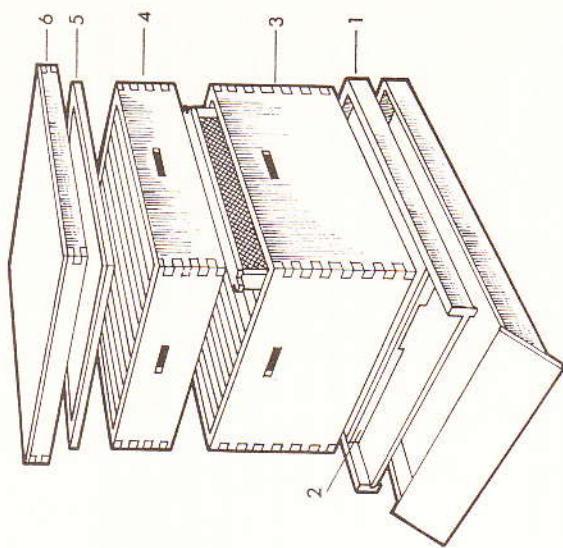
Colmena Perfección. 1, solería; 2, listón piquera; 3, primer cuerpo o cámara de cría; 4, segundo cuerpo o alza almacén de miel; 5, tablero interior; 6, cubierta tejadillo.
